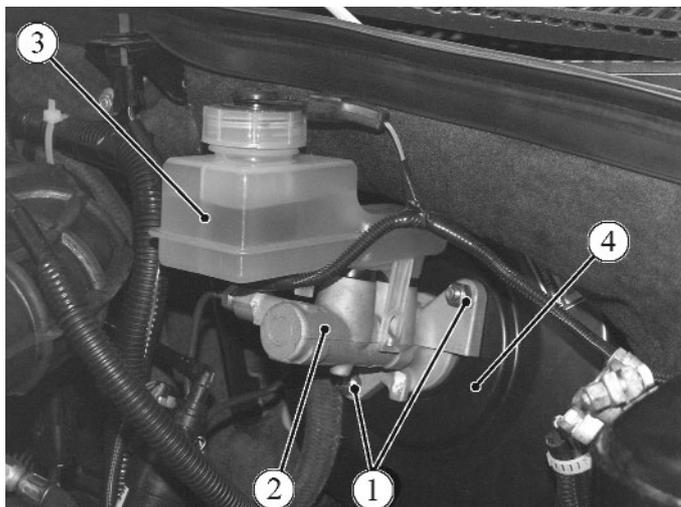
Вакуумный усилитель тормозов и главный цилиндр тормозов:
